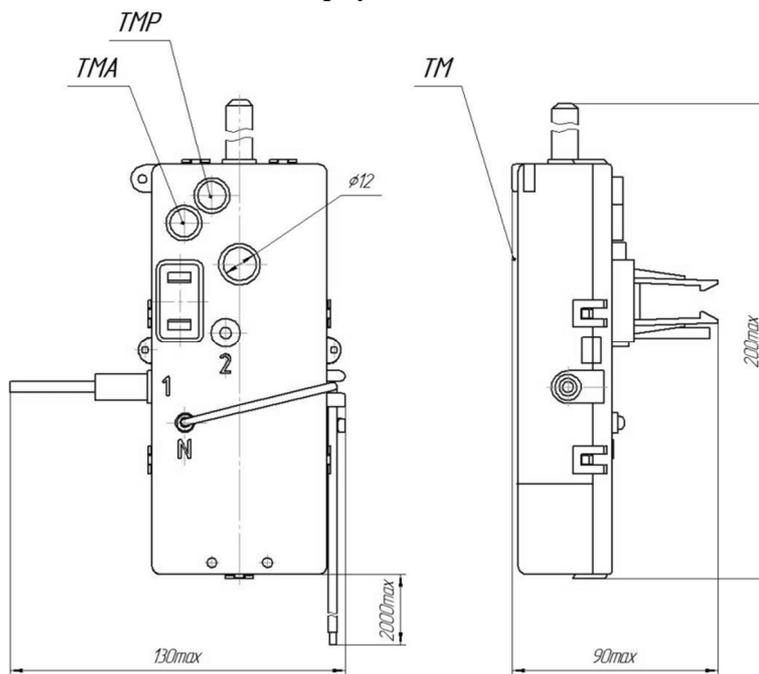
Габаритные и установочные размеры счетчиков, оснащенных УКН в корпусе «тип I»
